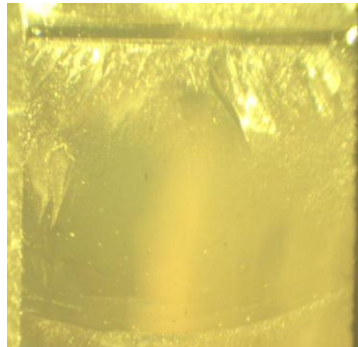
Superficie de fractura de una probeta del ensayo 9.
